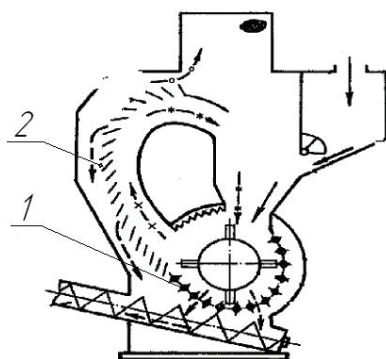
Конструктивно-технологическая схема дробилки ДЗ-6
